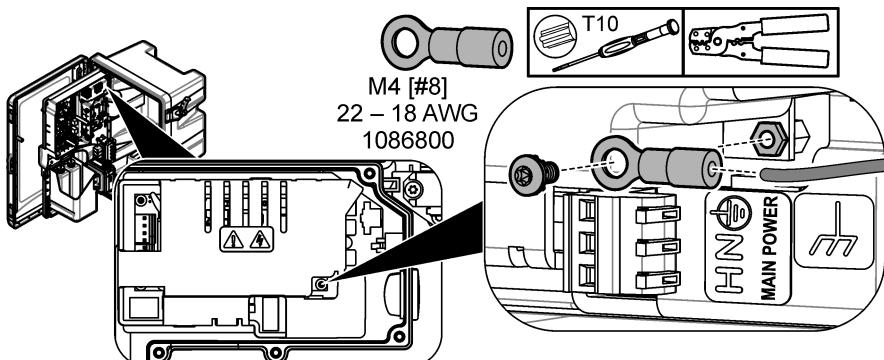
Zapojení kabelů – hlavní obvodová deska
